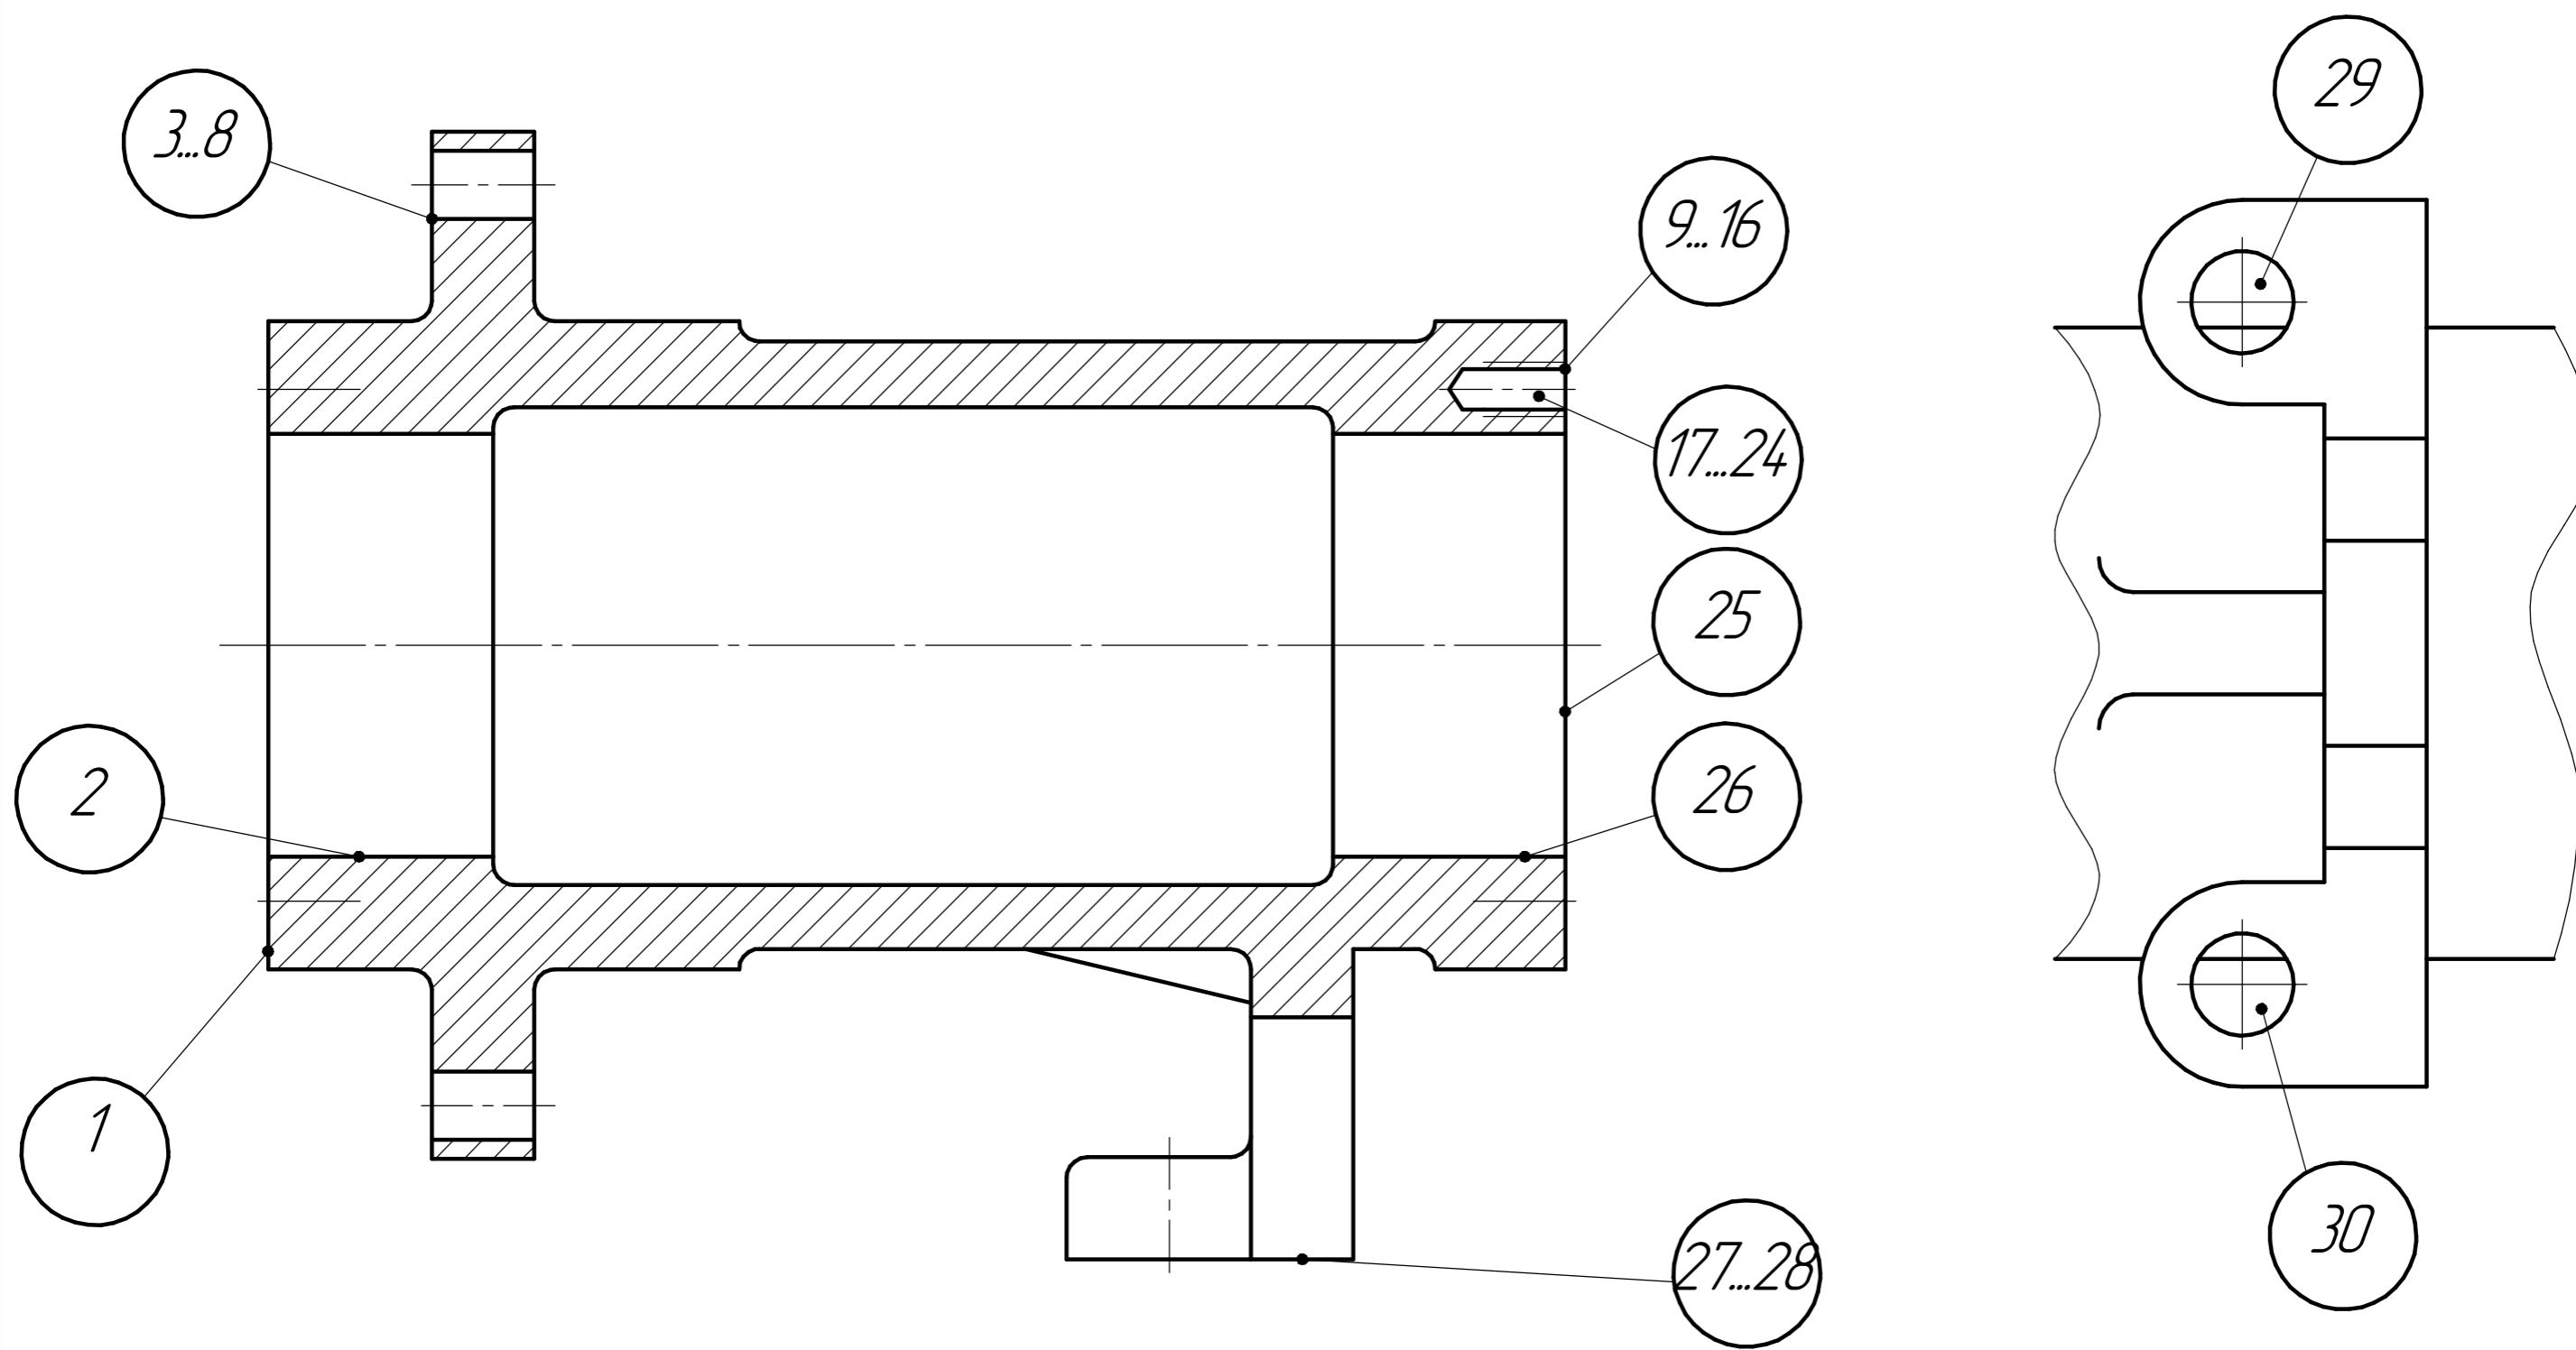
Ескіз деталі з номерами поверхонь
